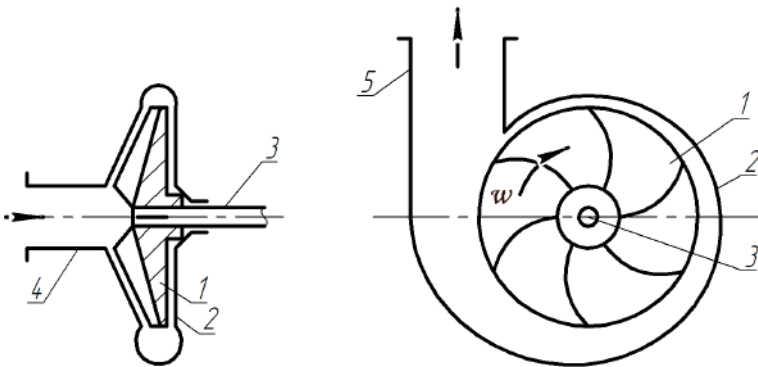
Схема центробежного насоса: 1 — рабочее колесо; 2 — корпус; 3 — вал; 4 — линия всасывания; 5 — линия нагнетания
